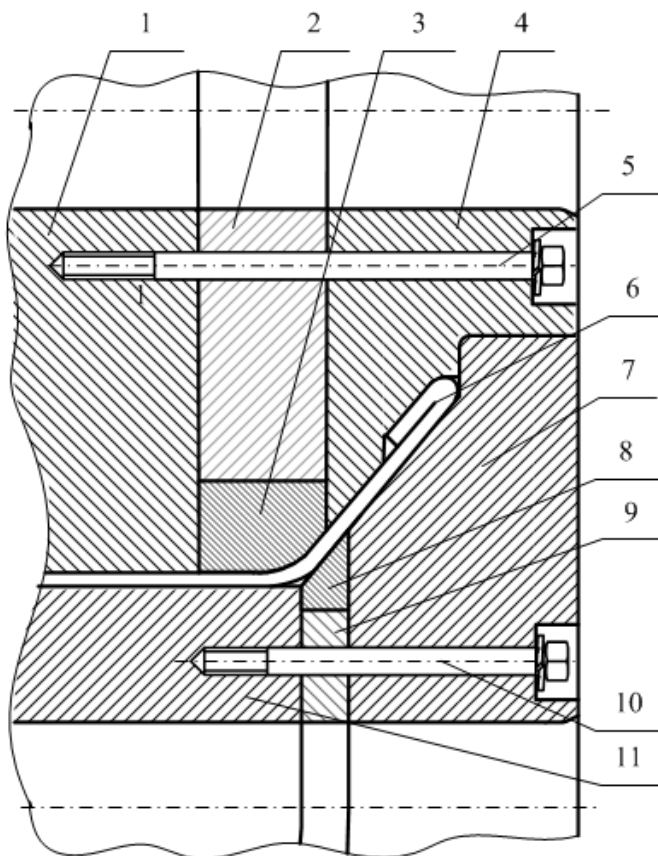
Конструкция вала с поворотными быстроизнашивающимися элементами
